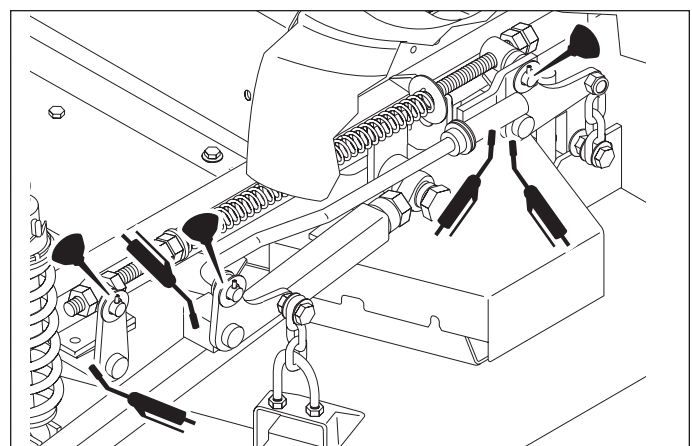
Pivotes de acoplamiento del elevador de cubierta
